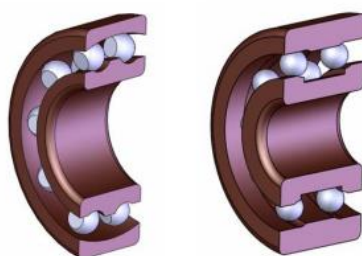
Самоустанавливающиеся подшипники качения
